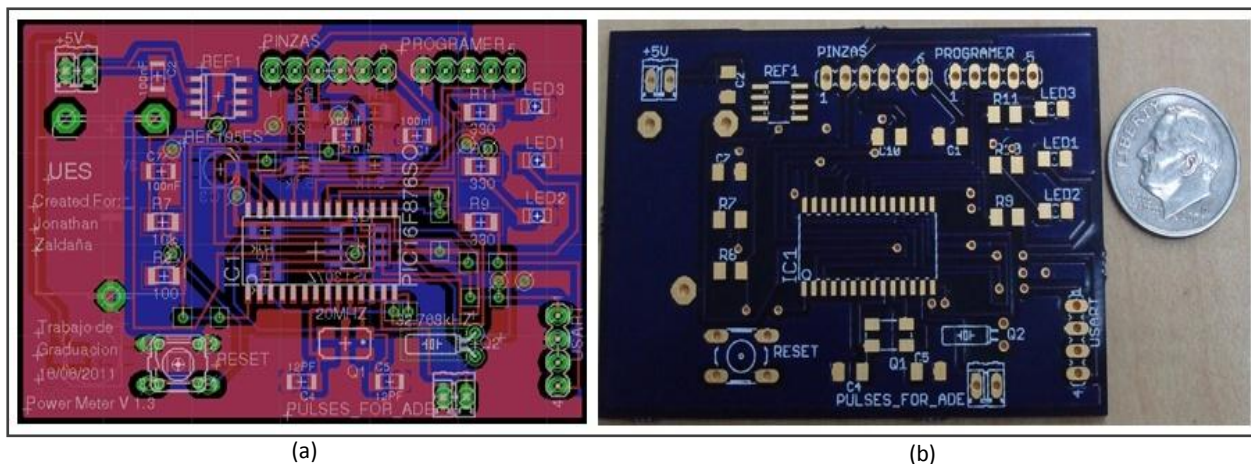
(a) Diseño del PCB; (b) Construcción del PCB.
